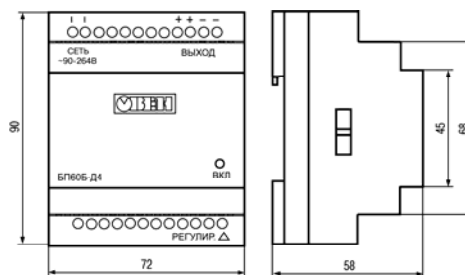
Габаритные размеры блока питания БП60Б-Д4-х
